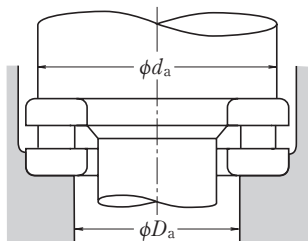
Диаметры опорной поверхности для упорных роликоподшипников
